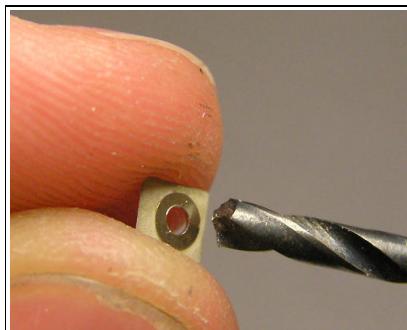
Das Loch beidseitig mit dem Bohrer entgraten.
